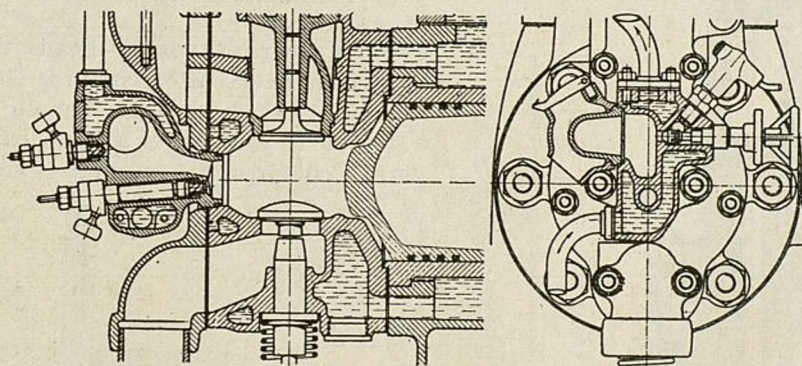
Motor Diesel horizontal Deutz, con encendido auxiliar eléctrico
